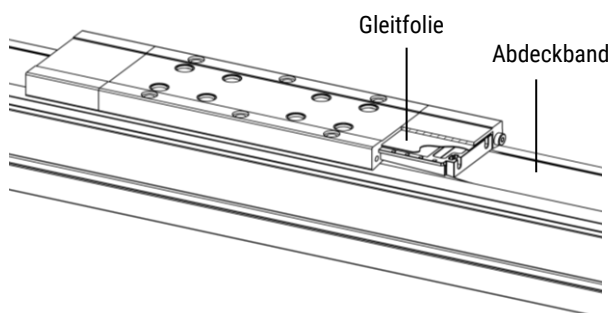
Demontage/Montage des Schlittenendstücks
